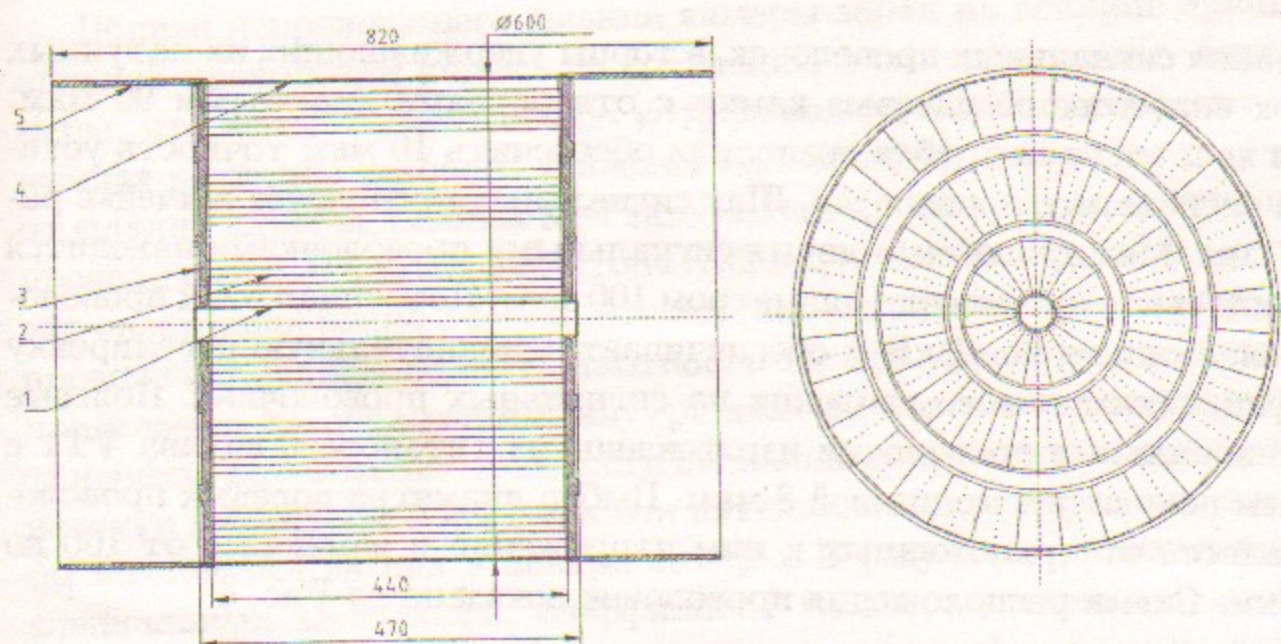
Схема дрейфовой камеры: 1 – герметизирующая трубка; 2 – проволочки; 3 – фланец; 4 – обечайка; 5 – кольца для поддержки кабелей.
